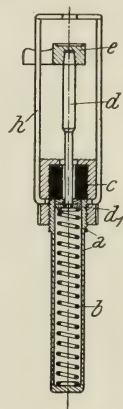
Selbstauslöser Autodrem (Ausführung Dr. E. MAYER, Wien). *a* äußeres Gehäuse mit Spiralfeder *b*; *c* Gummizylinder, *d* Kolbenstange mit Teller *d*<sub>1</sub>; *e* Auflager für den Drahtauslöser, *h* Drahtbügel. Länge des Gerätes zirka 11 cm, Gewicht zirka 15 g
